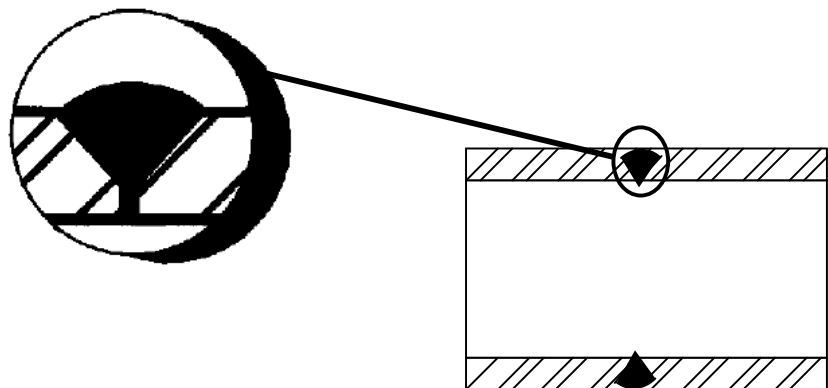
Soldadura de tubería con penetración incompleta (corrosión severa) ^[15].
